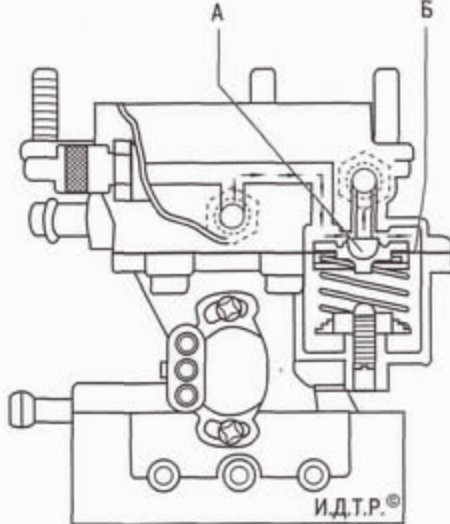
Регулятор давления топлива: А – редукционный клапан; Б – диафрагма
